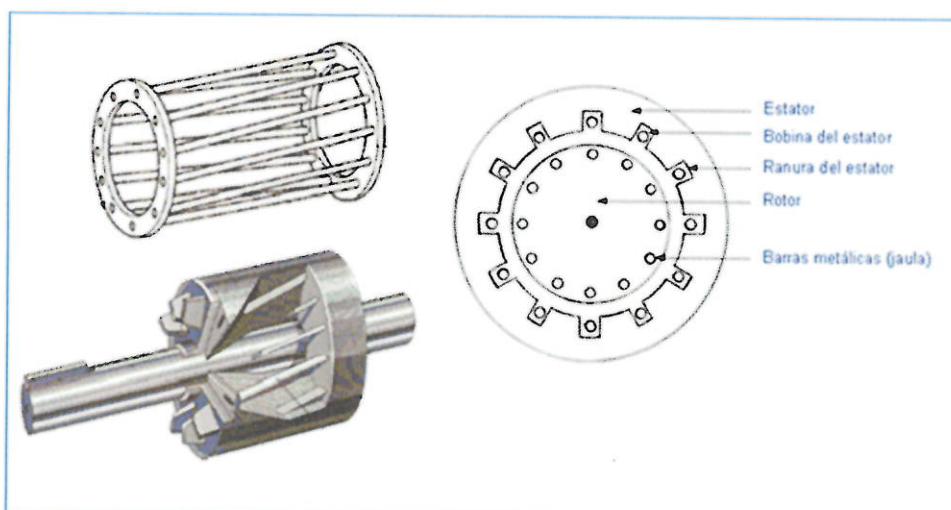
PARTES DE UN ROTOR DEVANADO.
